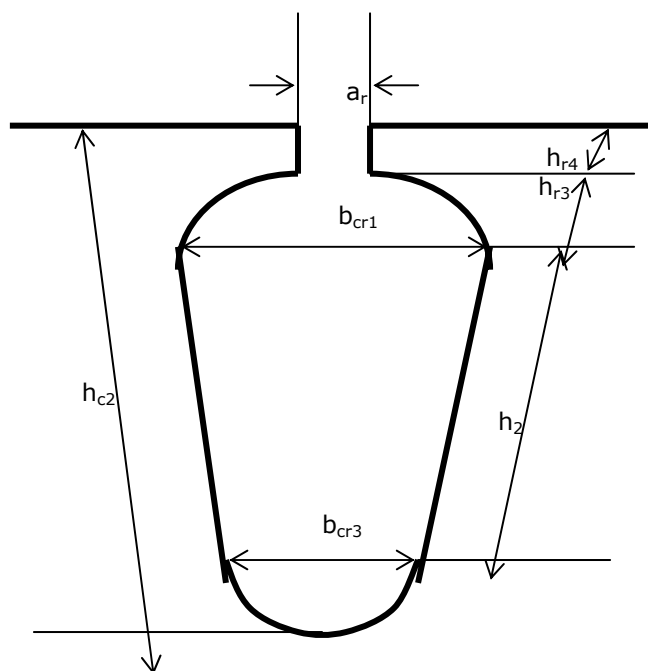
Creștătură ovală pentru colivie rotorică turnată din aluminiu.
